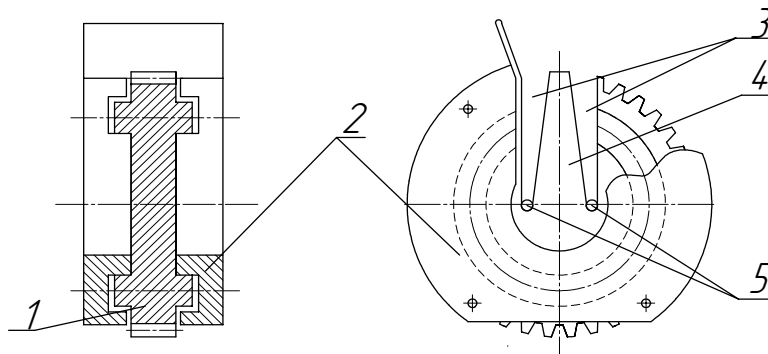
Скручуючий механізм шестерня з пальцем:
